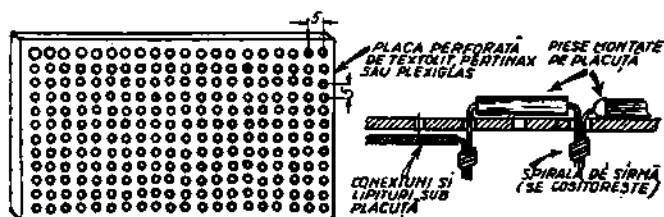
Placa de montaj și modul de asamblare al pieselor.
